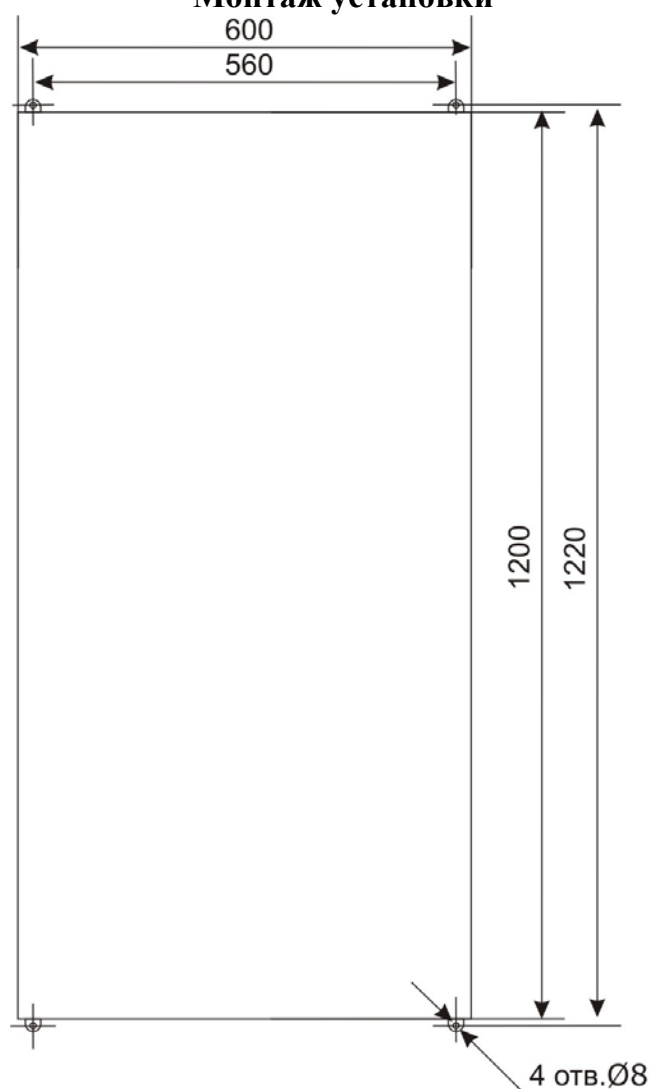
Координаты отверстий для крепления каждого блока детектирования на стену
